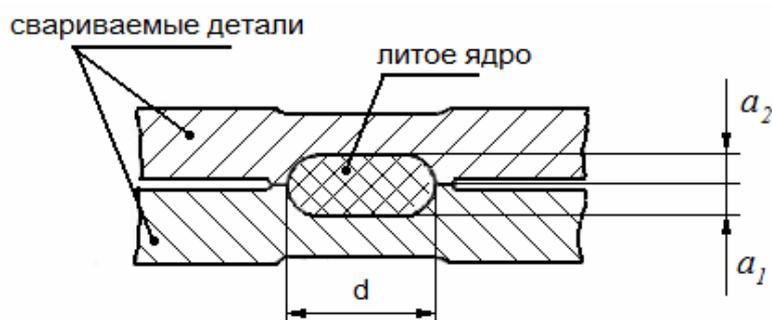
Схематический разрез точечного сварного соединения:  $d$  – диаметр литого ядра,  $a_1$ ,  $a_2$  – глубина проплавления свариваемых деталей
